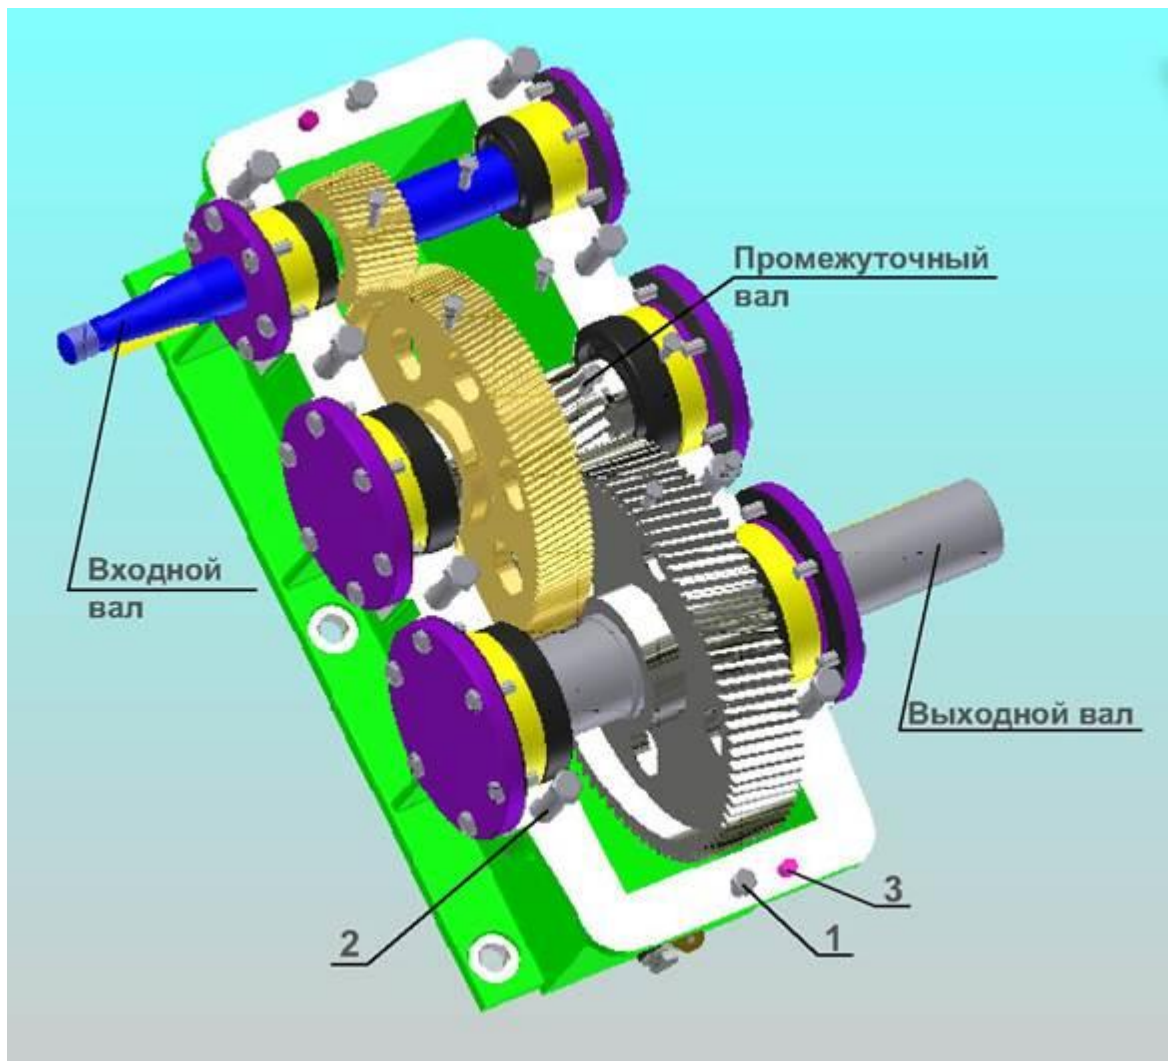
Внешний вид редуктора без крышки: 1 – болты крепления крышки и корпуса редуктора; 2 – болты для соединения корпуса и крышки редуктора, установленные в бобышки (приливы у подшипниковых узлов); 3 – штифты для фиксации крышки
